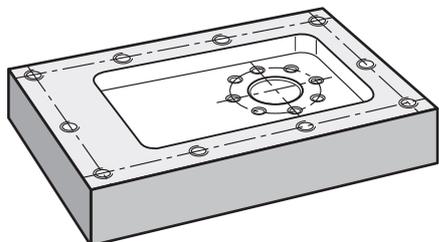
Образцовая деталь – Изготовление ряда из отверстий
